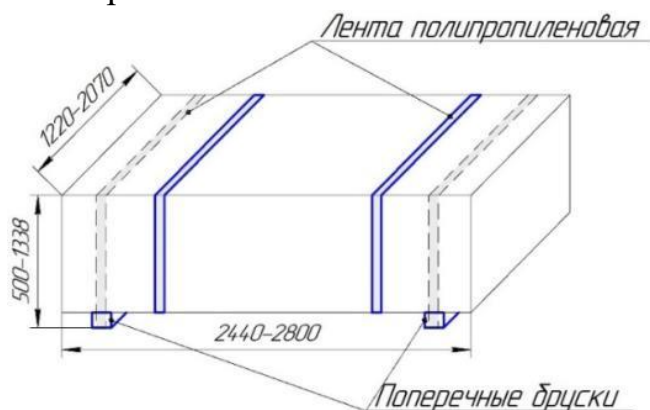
Вид транспортного пакета размером 1220-2070x2440-2800мм
